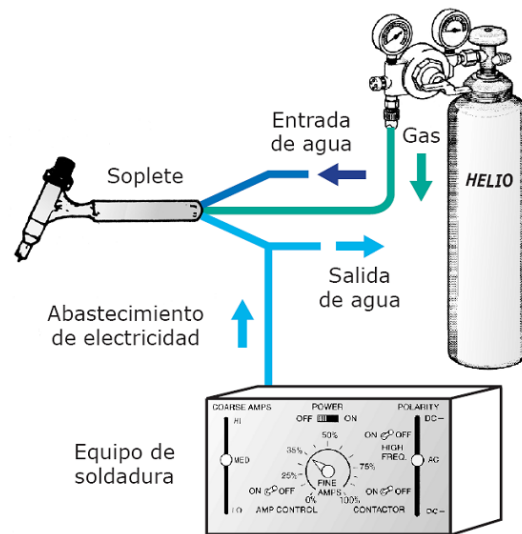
Esquema de un sistema para soldadura de arco TIG.
